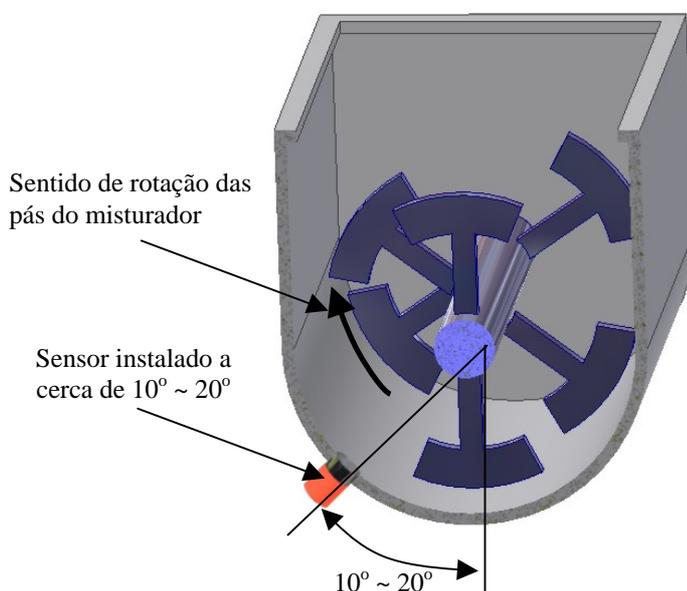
Posição para a instalação do sensor de umidade num misturador de eixo horizontal. É importante observar o sentido de rotação das pás e o lado correto para montagem do sensor.
